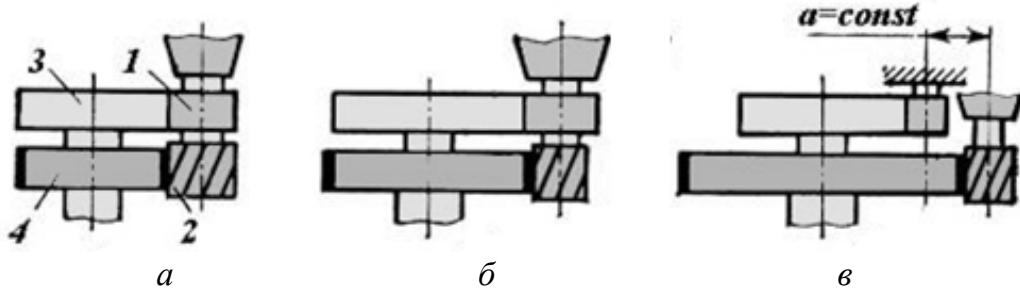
Схемы фрезерования поверхностей с криволинейным замкнутым контуром:
